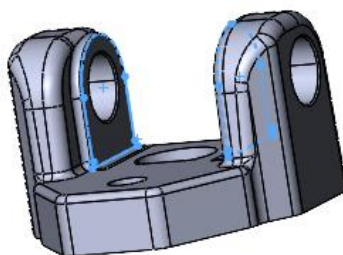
Деталь з створеними 2-ма ескізами на гранях вух для побудови заготовки.
